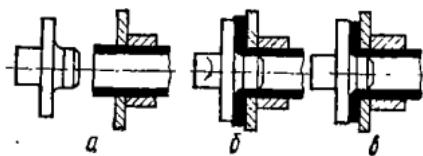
Схема отбортовки труб из фторопласта без внешнего нагрева:
